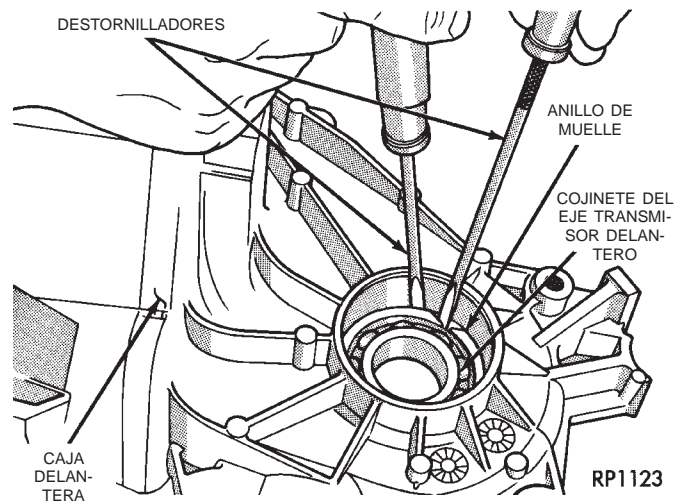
Desmontaje del anillo de retención del cojinete del eje transmisor delantero
